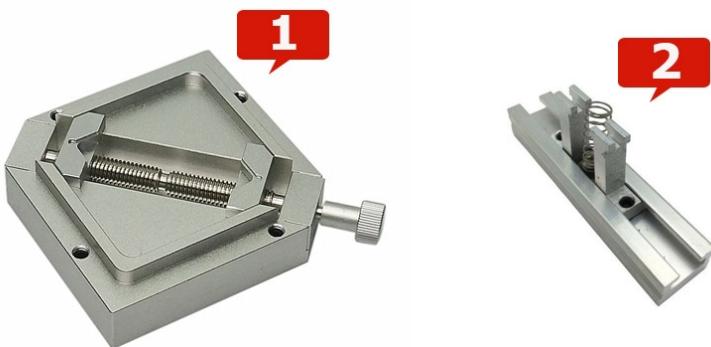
suporte BGA Honton Ht 90x90 (1) e suporte universal simples (2)
